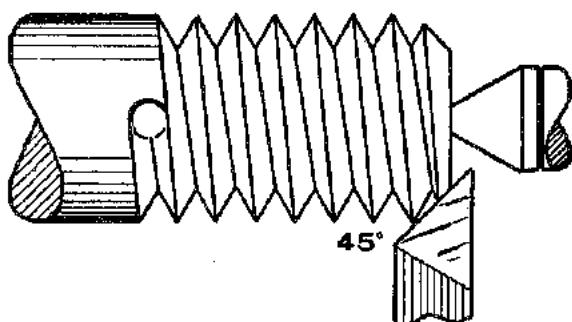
Debe achaflanarse el extremo de la pieza roscada (South Bend Lathe Works).
